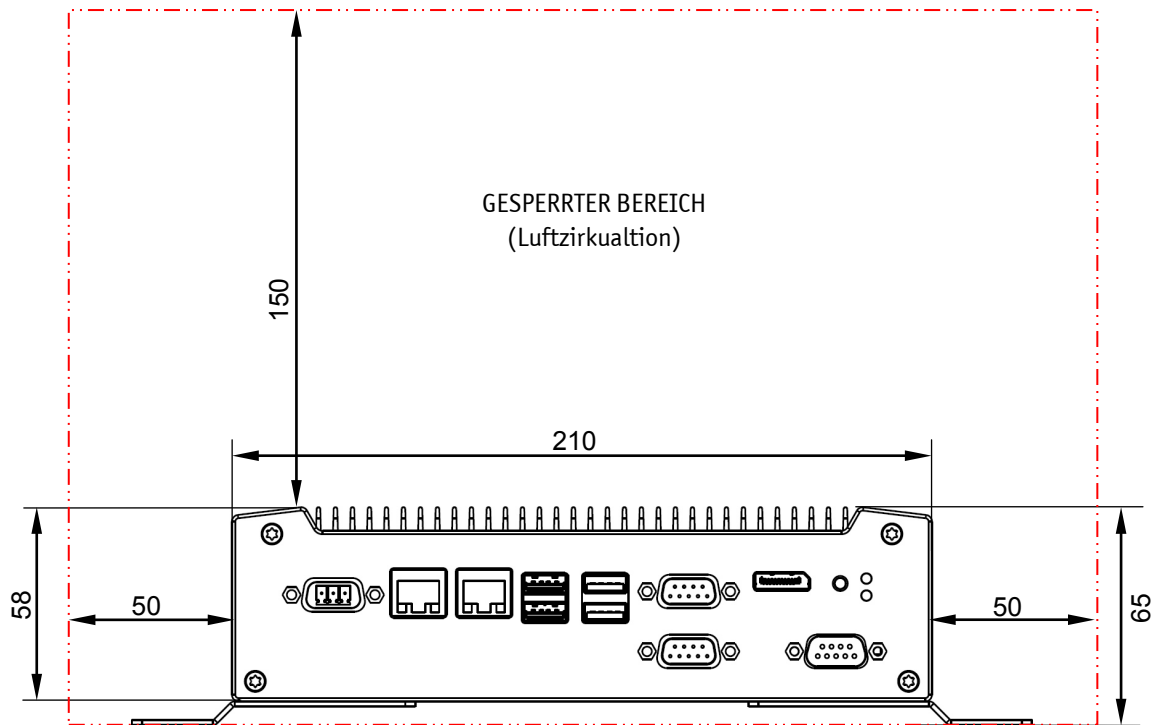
Maßangaben in der Frontansicht (Wand- oder Tischmontage)
